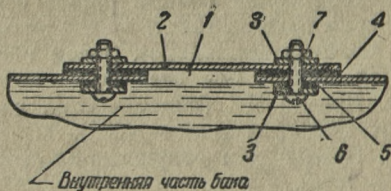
Постановка заглушки в стенке бака при заделке пробойны:
